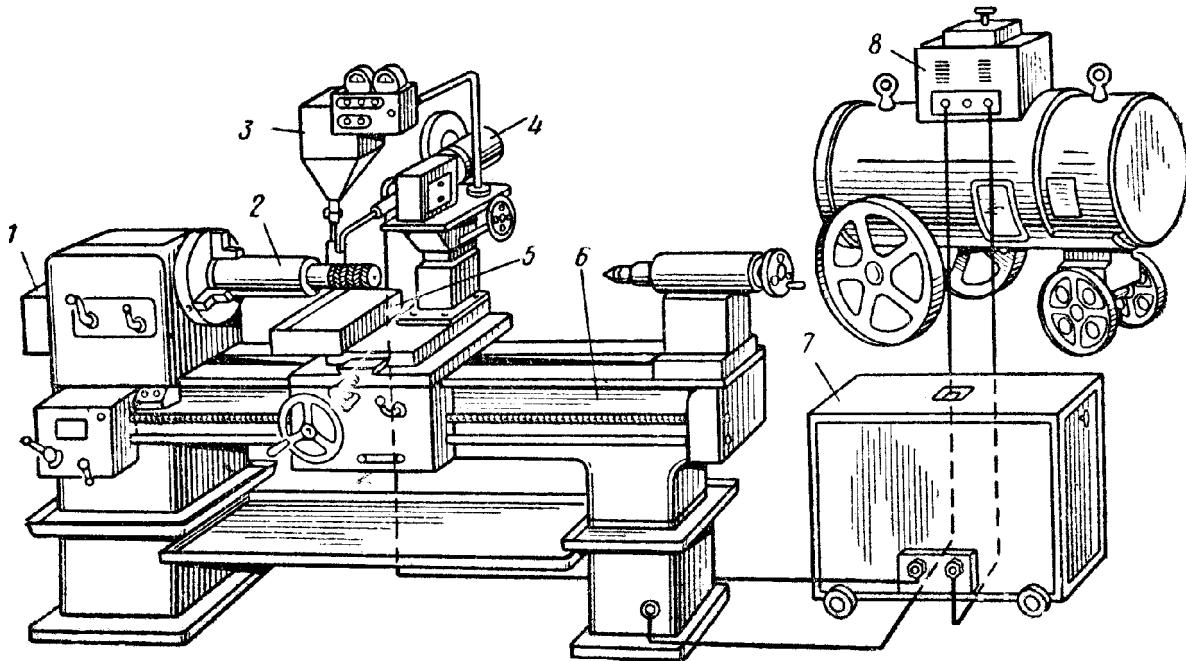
Схема установки для автоматической наплавки под слоем флюса: 1 – замедляющий редуктор; 2 – наплавляемая деталь; 3 – бункер для флюса; 4 – наплавочный аппарат; 5 – поддон для шлаковой корки; 6 – токарный станок; 7 – аппаратный ящик; 8 – сварочный преобразователь
